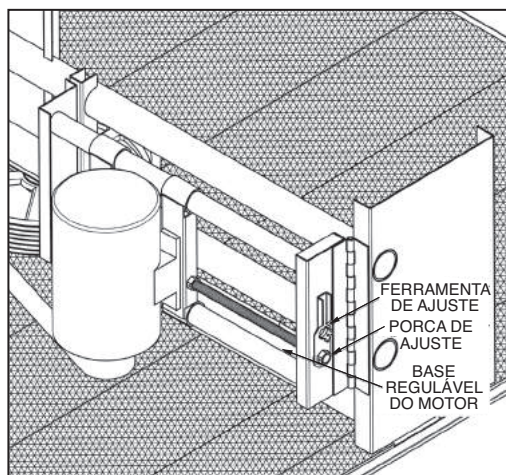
Motor Montado Internamente, Tiragem Induzida
